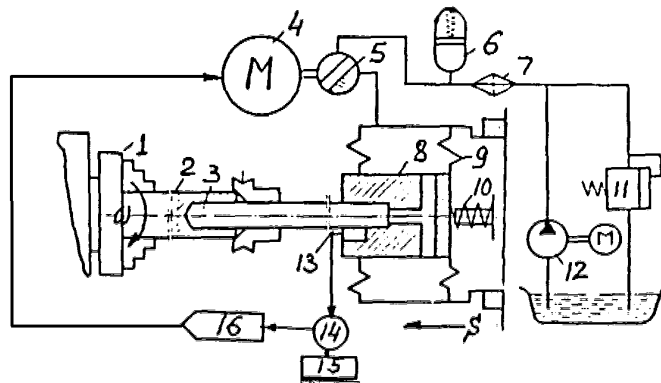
Верстатна система, призначена для свердління рушничними свердлами
